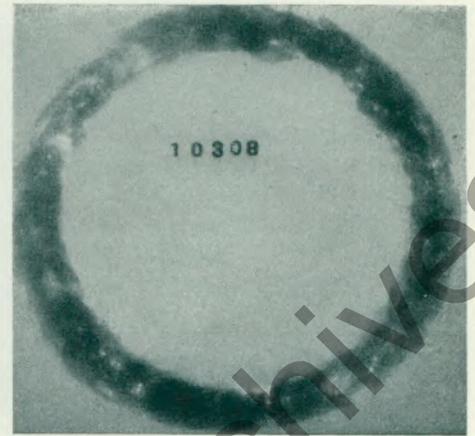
Beispiel einer guten Kreis Schweißung.
